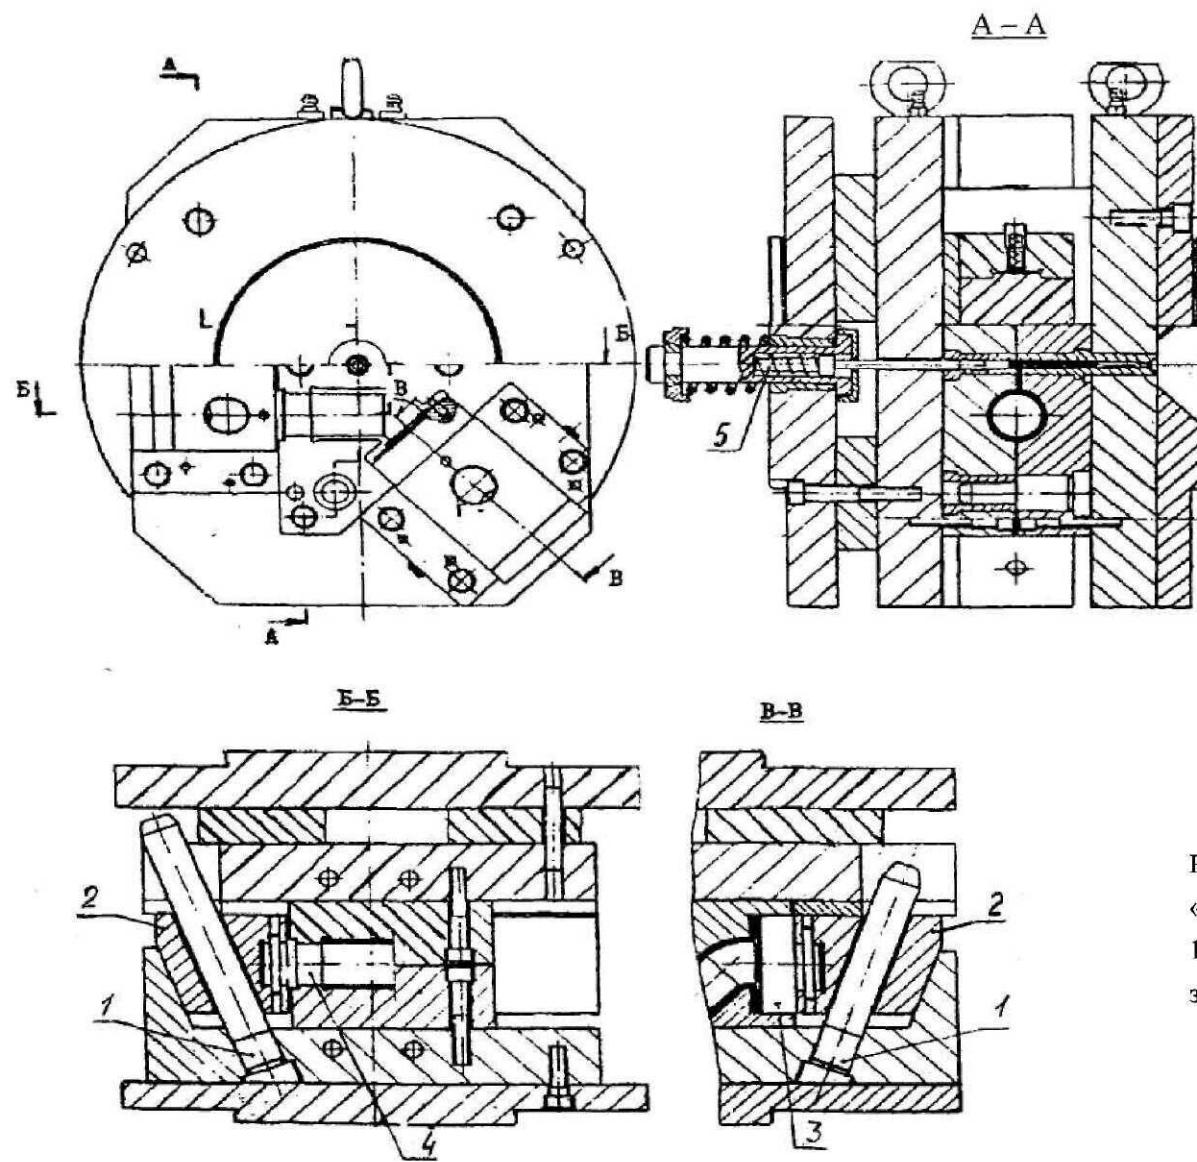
Пресс-форма для изготовления детали «угловой патрубок»:
